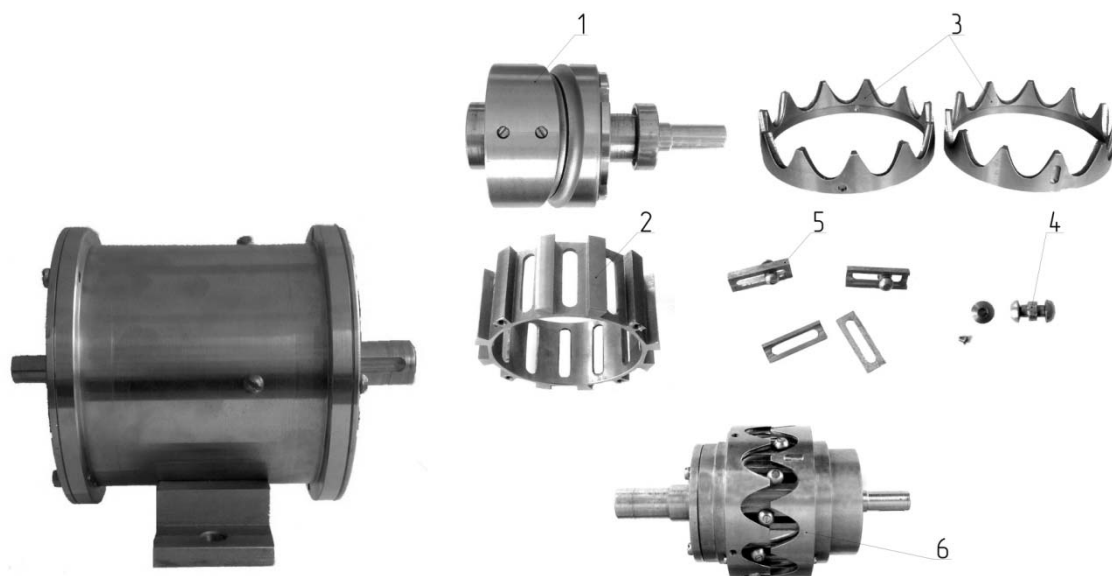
Опытный образец и детали ЦКРП: 1 – ведущий вал с кулачками, образующими однопериодную беговую дорожку; 2 – сепаратор со сквозными продольными прорезями, являющийся элементом ведомого вала; 3 – кулачки, закрепляемые в корпусе и образующие многопериодную беговую дорожку; 4 – составные ролики; 5 – вкладыши с составными роликами; 6 – редуцирующий узел ЦКРП
